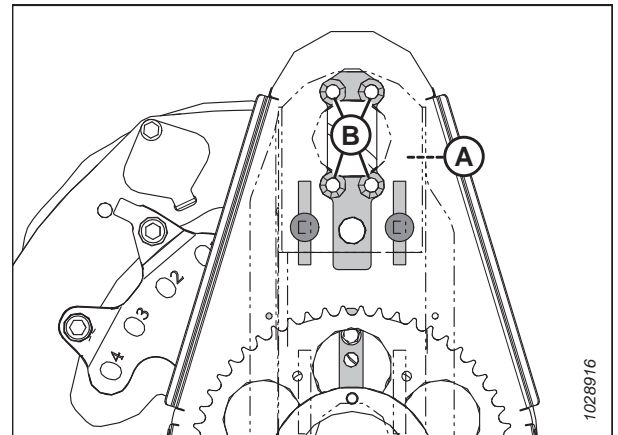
Fori di montaggio del motore di trasmissione dell'aspo
